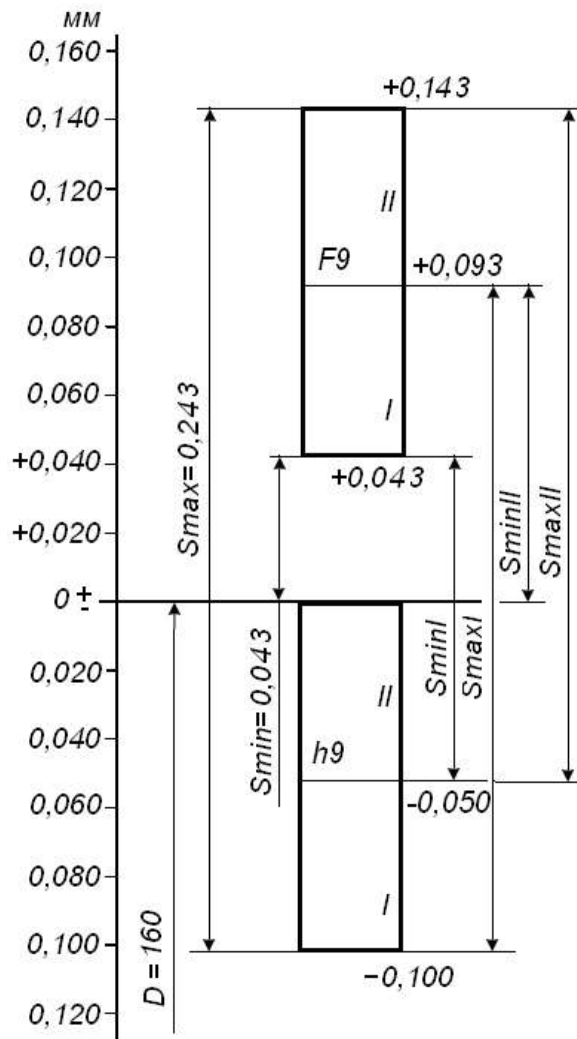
Схема розташування полів допусків з'єднання Ø160F9/h9
